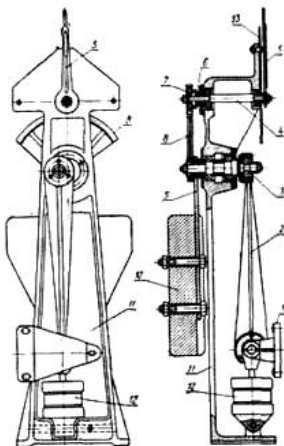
Маятниковий ваговий механізм електростенду ГОСНИТИ: 1 – кронштейн для з'єднання механізму з корпусом електричної машини; 2 – тяга від корпусу машини до ексцентрикового валика; 3 – ексцентриковий валик; 4 – валик стрілки циферблату; 5 – стрілка циферблату; 6 – втулка з торцевими зубцями; 7 – шестерня мала; 8 – шестерня велика; 9 – важіль маятника; 10 – вантаж маятника; 11 – стійка; 12 – демпфер; 13 – пульт приладів.
